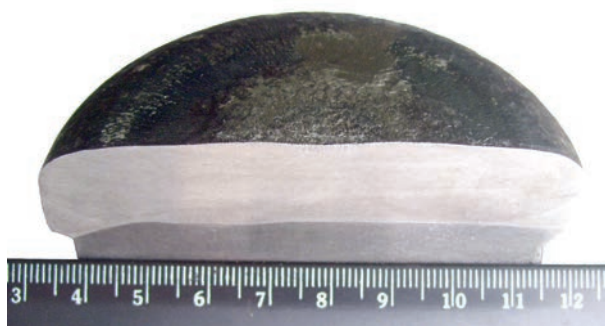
Макрошлиф заготовки, наплавленной нетоковедущей порошковой проволокой ПП-Нп-25Х5ФМС диаметром 3 мм в ТПК диаметром 85 мм
